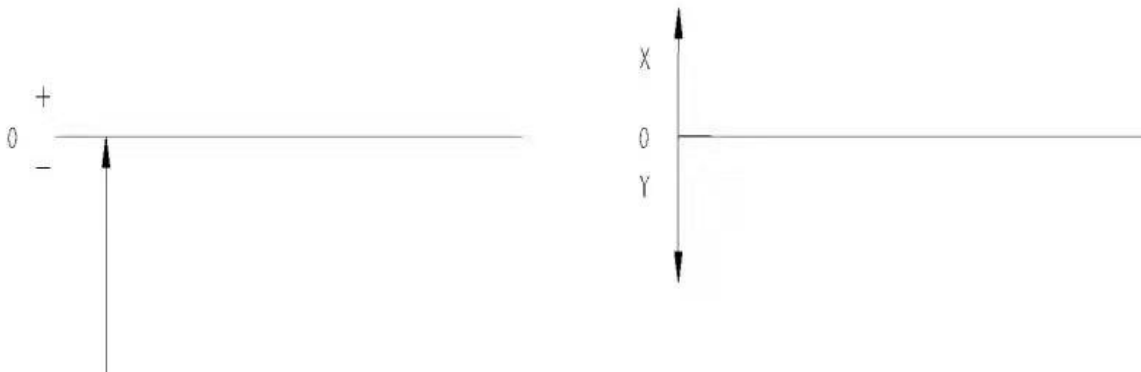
轴承外圈与轴套内孔配合公差图
